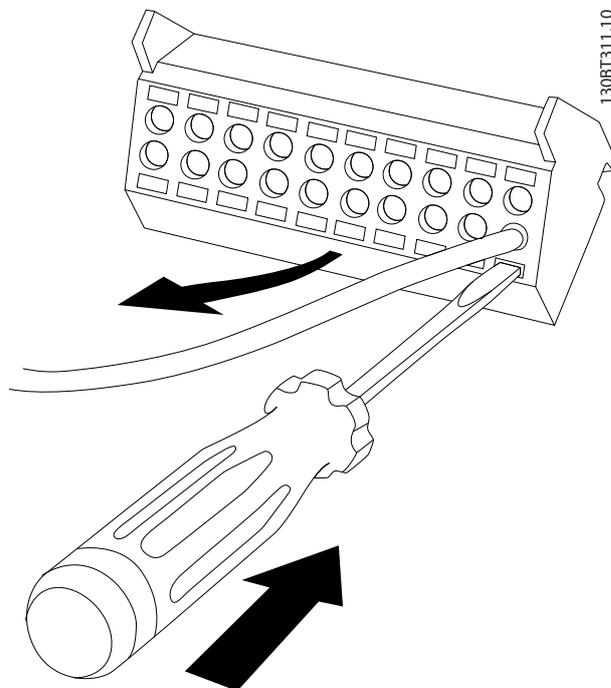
Removendo a Chave de Fenda após Inserção do Cabo
